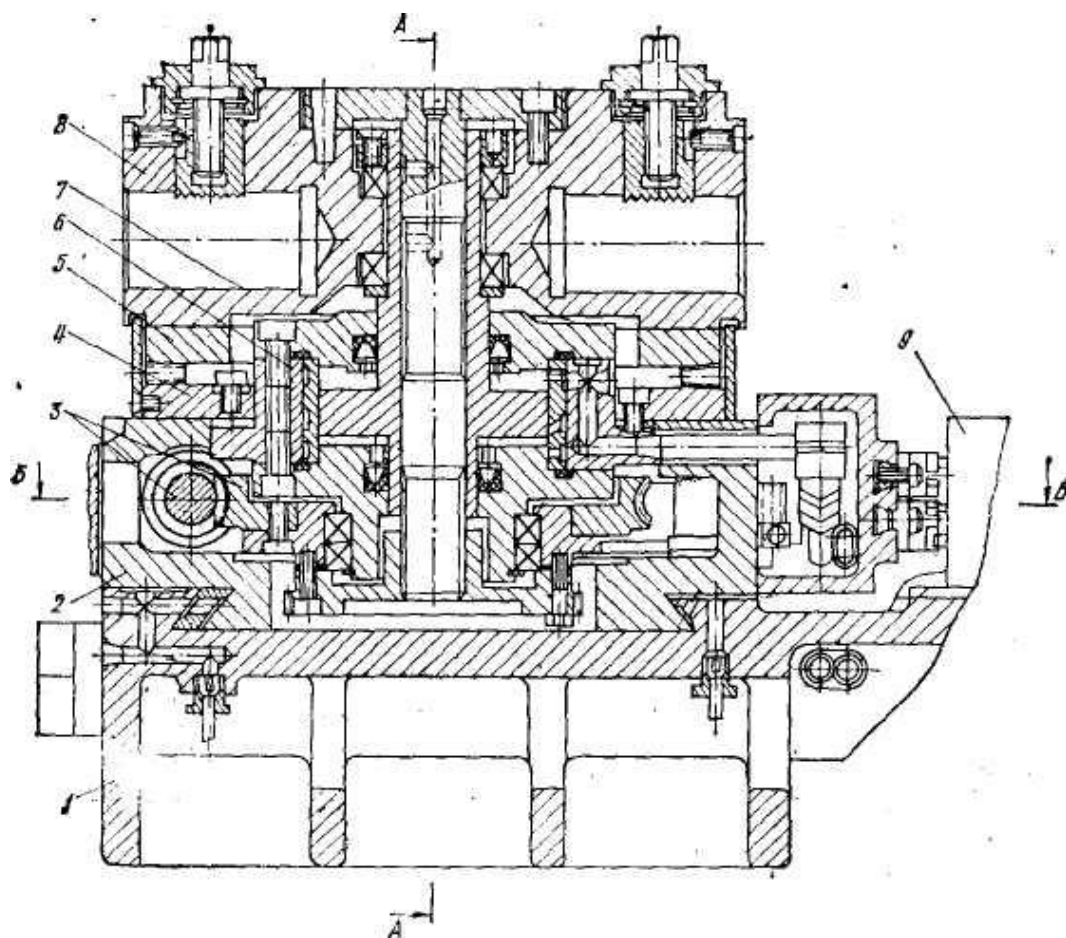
Конструкция револьверного суппорта станка 1В340Ф30
